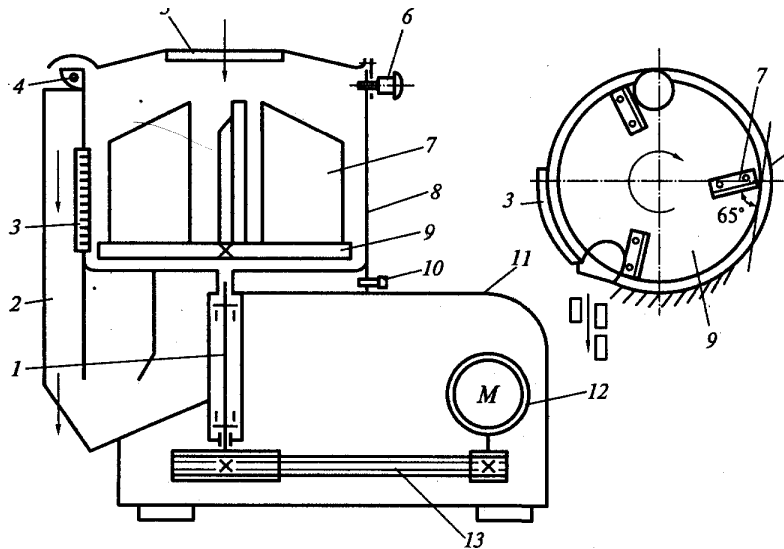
Принципова схема роторної овочерізальної машини:
